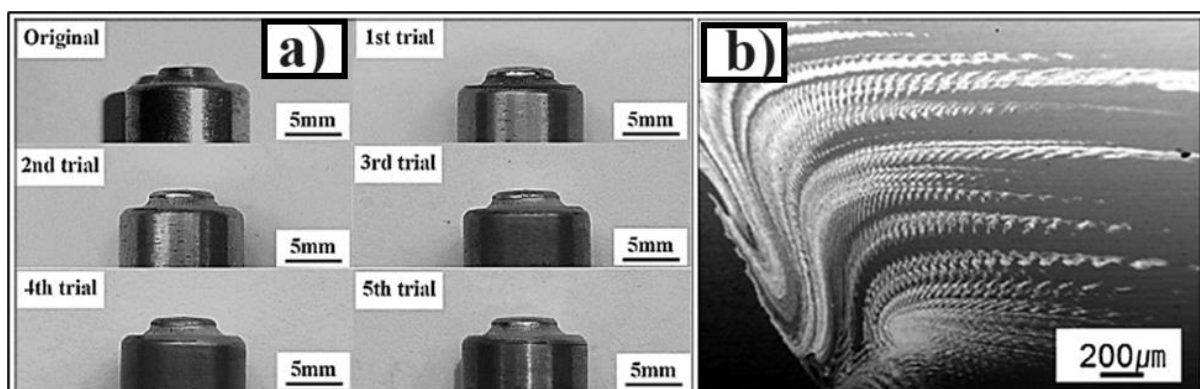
a) Desgaste da ferramenta após cada ensaio; b) presença de fragmentos da ferramenta na zona de soldadura [18].
